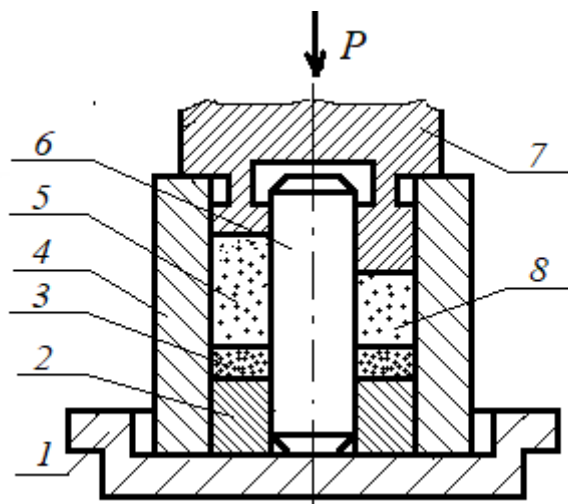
Изготовление ААИ типа 2А2 прессованием:
